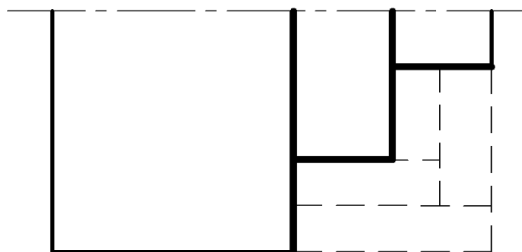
Схема удаления припуска заготовки в случае комбинирования направлений перемещений резца
